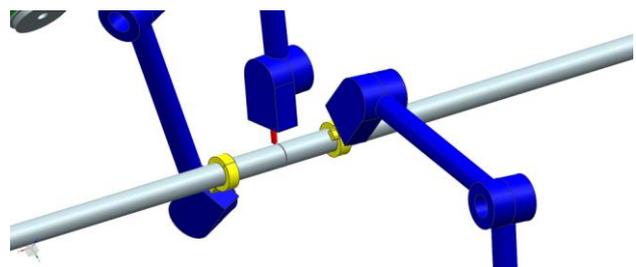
Пример расположения манипуляторов при сварке
